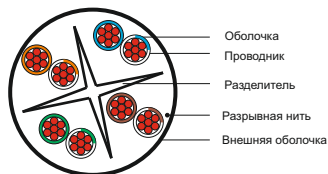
Конструкция кабеля типа U/UTP с многопроволочными жилами
